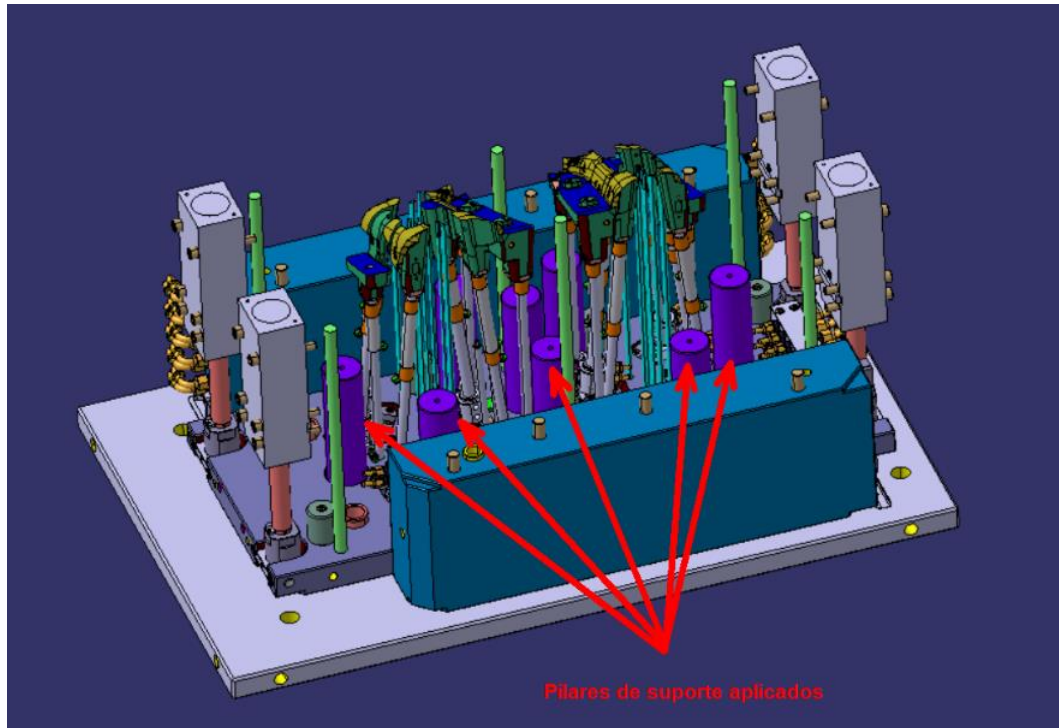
Pilares de suporte aplicados no molde em estudo.
